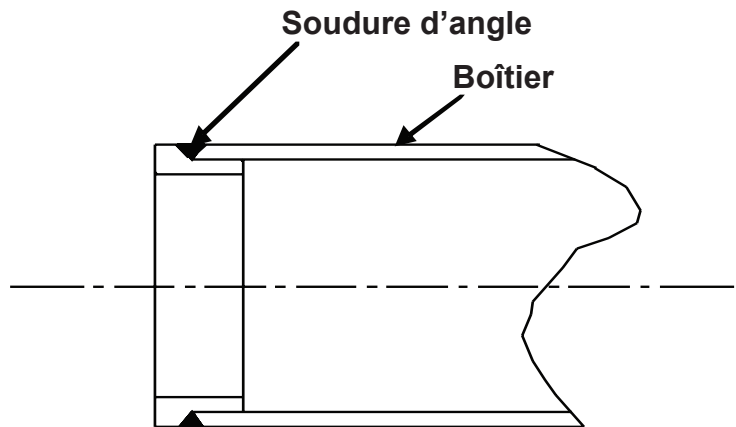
Type d'épaulement, Sabot, Soudure d'angle
